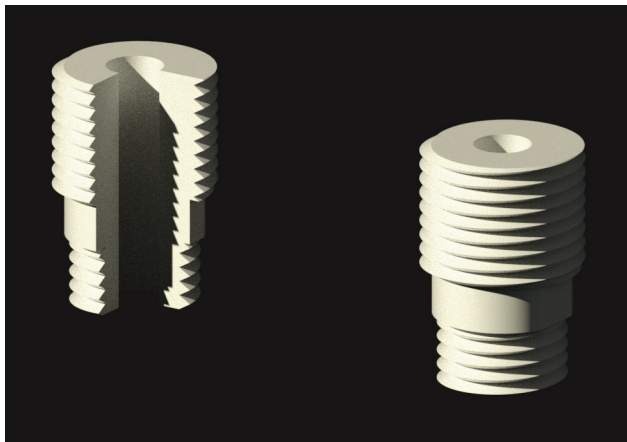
Detalle de las piezas de aislamiento eléctrico.
